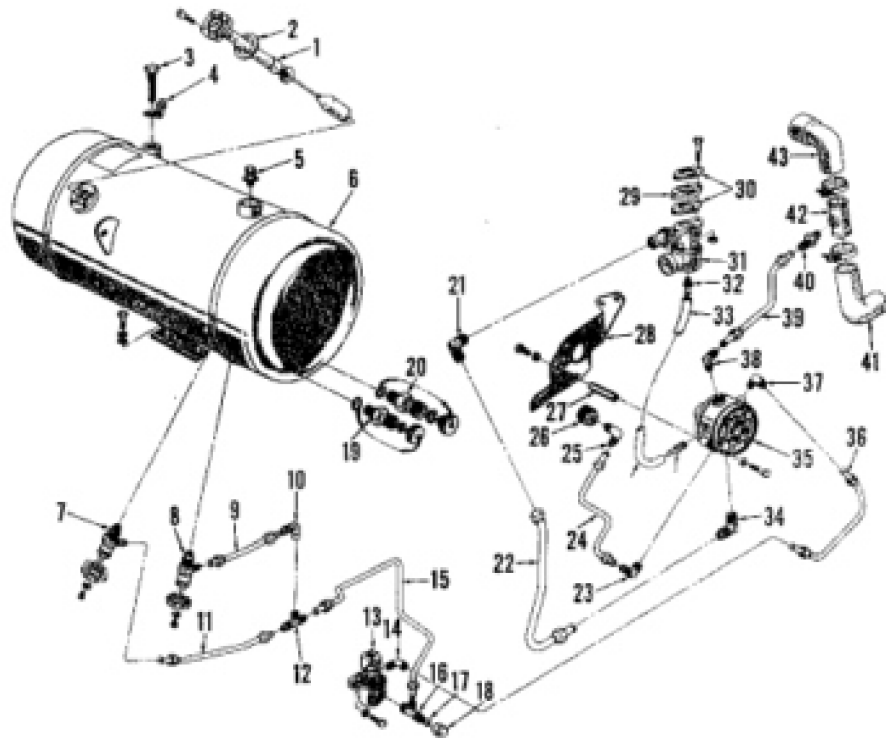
Geëxplodeerd beeld van het LP-Gas systeem dat op model 4000 trekker wordt gebruikt. Refer to Fig.109 for exploded view of filter-fuelock assembly (13); to Fig. 107 for exploded view of carburetor (31) and to Fig. 110 for exploded view of converter (vaporizer-regulator) (35).
